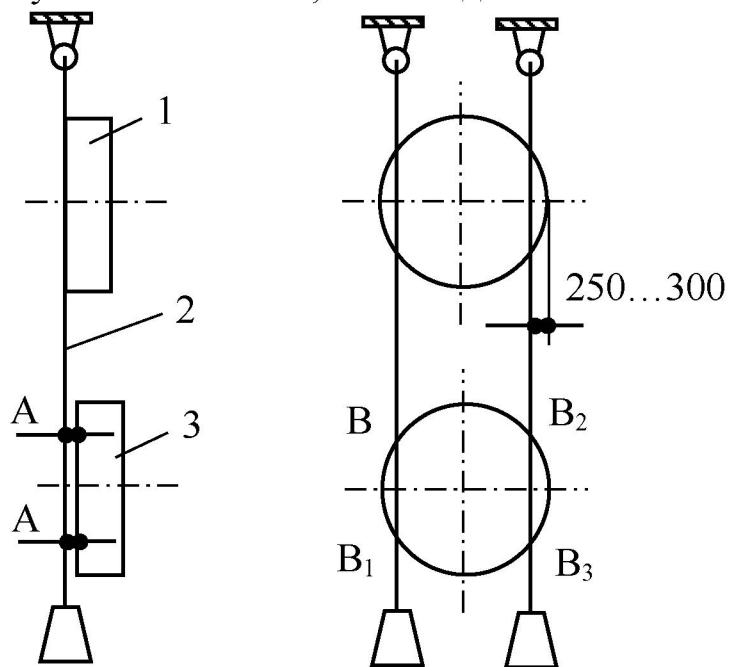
Схема проверки параллельности торцовых поверхностей шкивов
